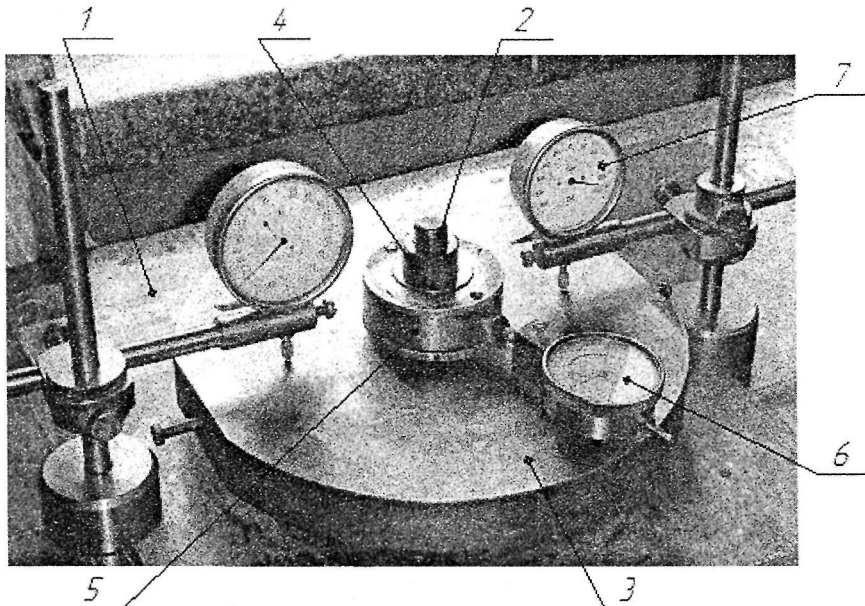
Установка для определения смещений заготовки под действием сил закрепления при базировании по плоскости: 1 — основание; 2 — центральный винт; 3 — заготовка; 4 — гайка; 5 — динамометр сжатия; 6, 7 — индикаторы
